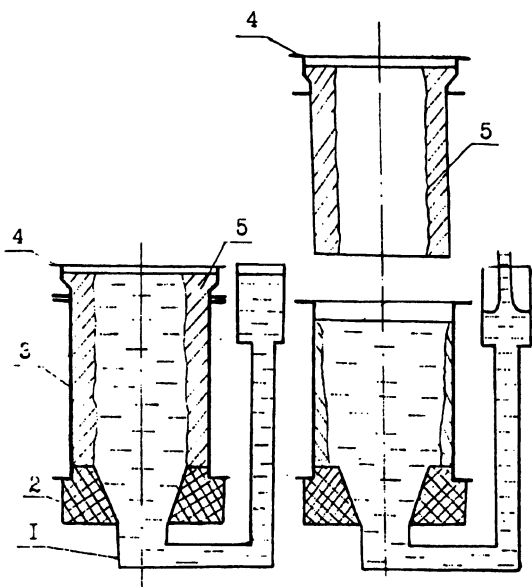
Принципиальная схема непрерывно-циклического литья намораживанием: 1 — металлопровод; 2 — соединительный стакан; 3 — кристаллизатор стационарный; 4 — кристаллизатор подвижный; 5 — отливка
